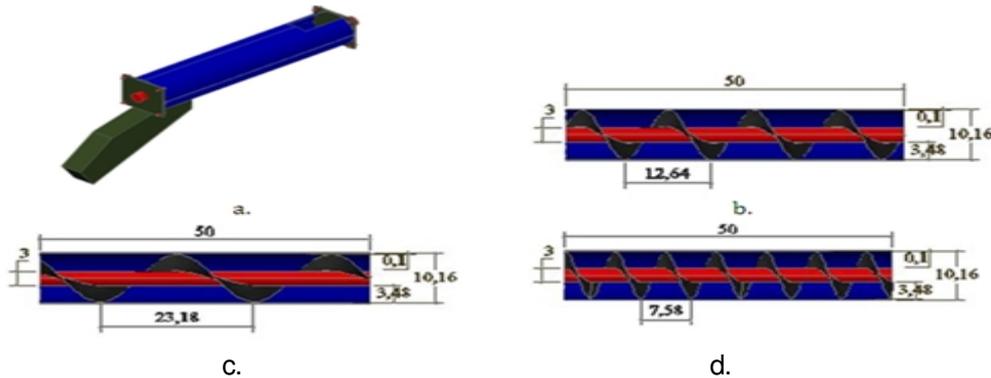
Kerangka *screw conveyor* tampak samping dan atas beserta dimensi (cm)
